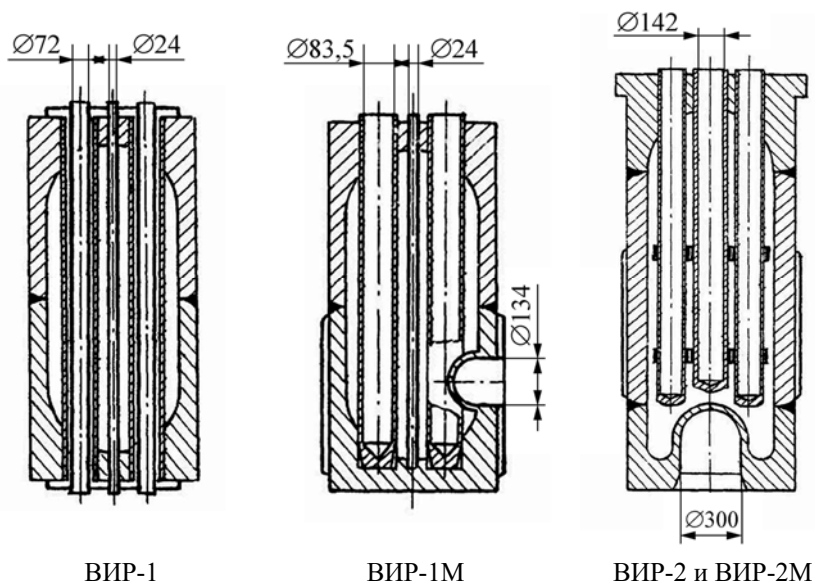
Конструктивная схема корпуса АЗ реактора типа ВИР
